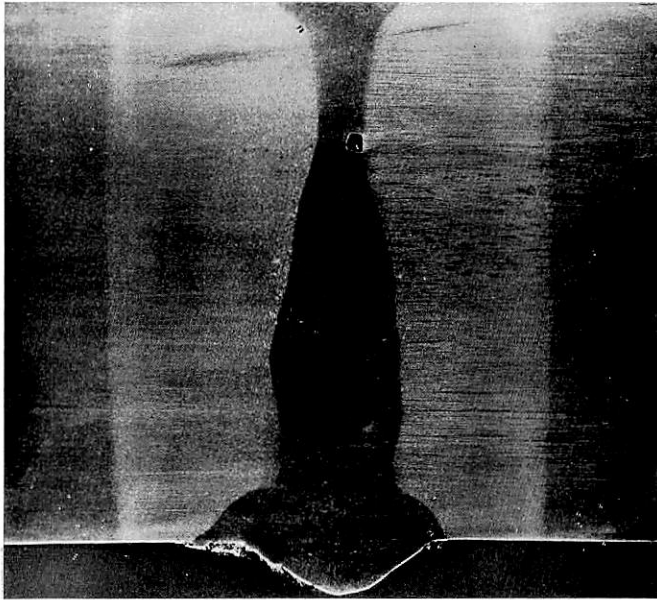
Zwischengußschweißung ohne Stauchung, ungeglüht.
